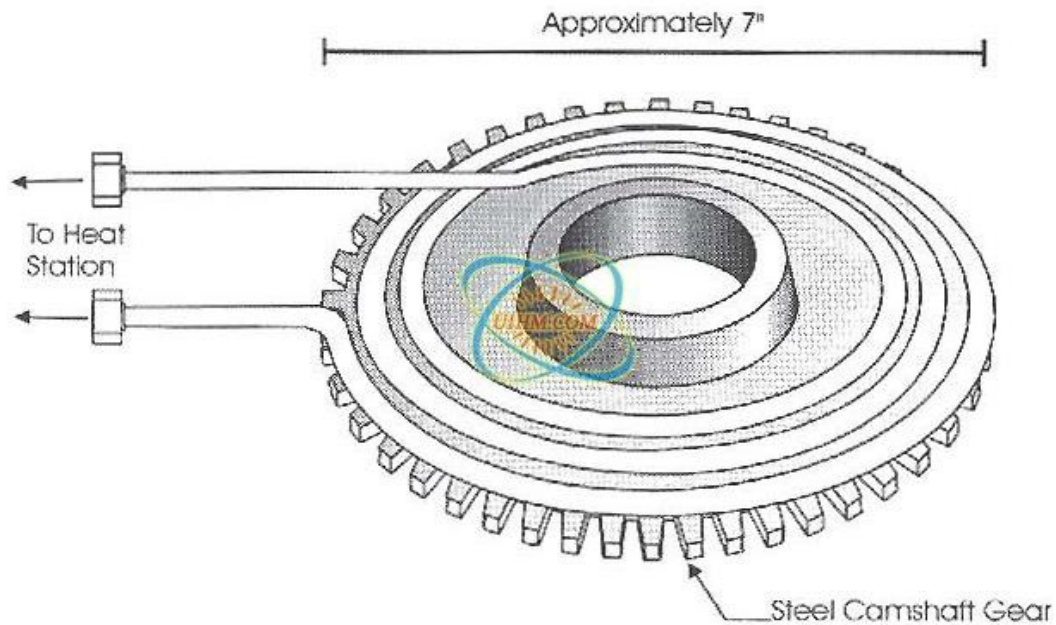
Ajuste del árbol de levas engranaje. [F-37]
